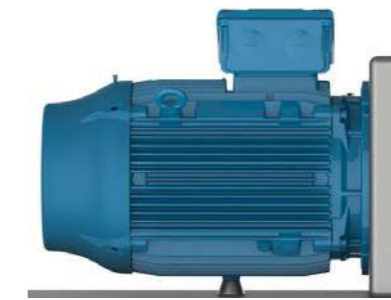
Representação da fixação do motor com flange e apoio na base da carcaça.
